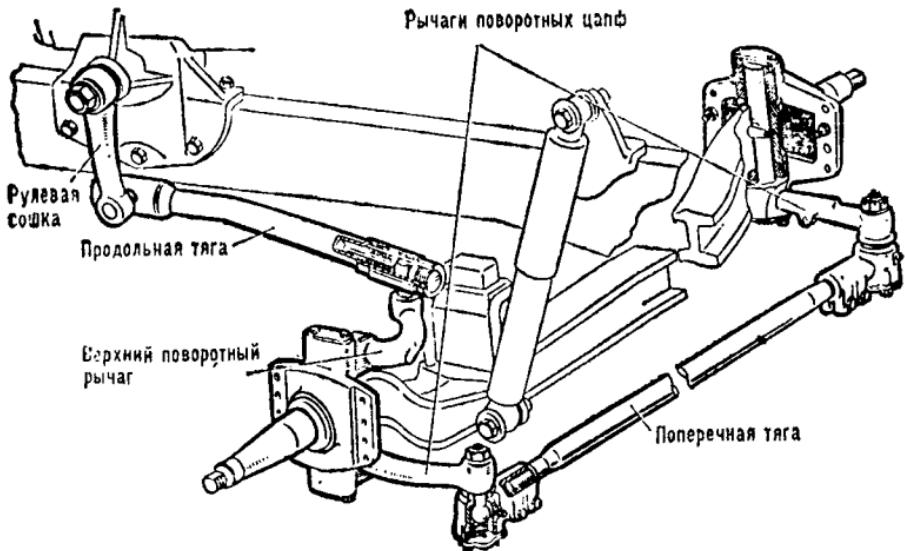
Привод рулевого управления автомобиля ЗИЛ-130
